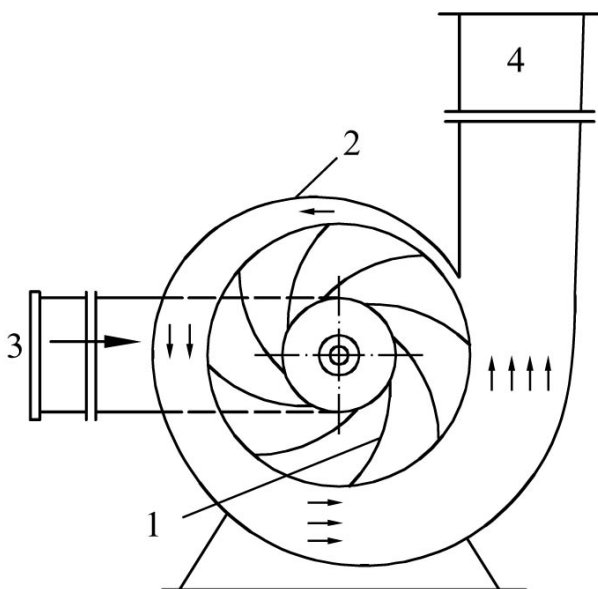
Схема устройства центробежного нагнетателя: 1 – лопасти; 2 – кожух; 3 – всасывающий патрубок; 4 – напорный патрубок
